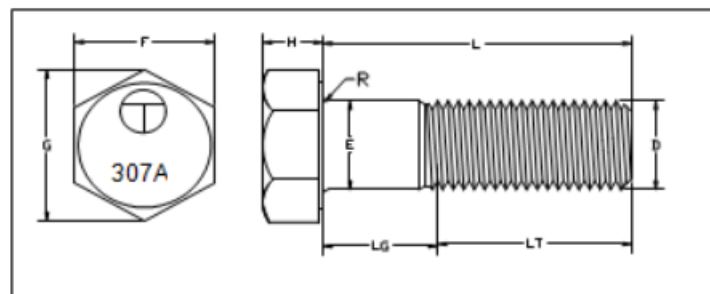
Dimensiones del tornillo ASTM A307 de la empresa TORMEX¹³
